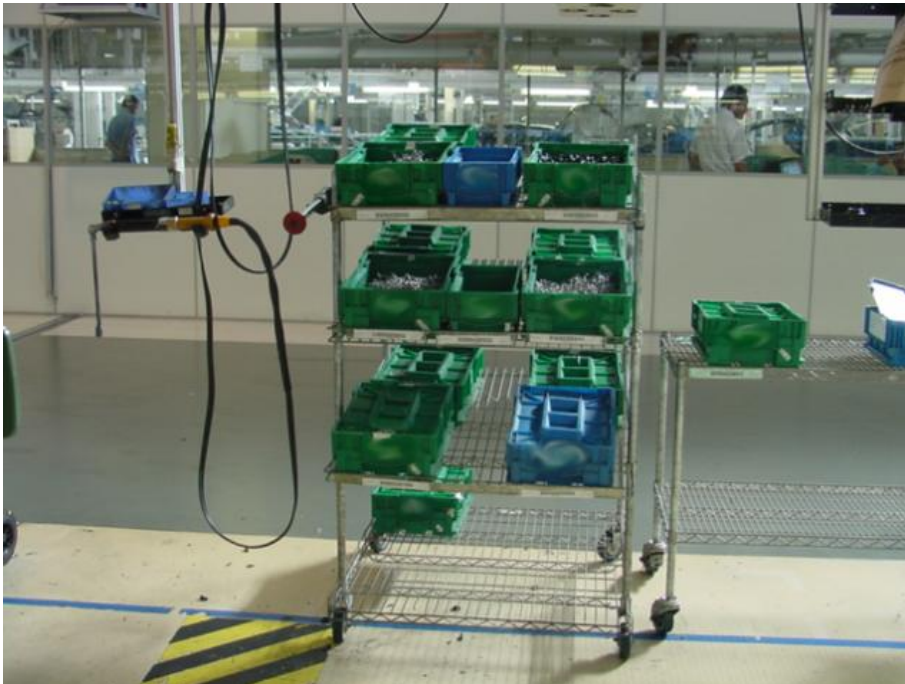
Abastecimento de peças ergonomicamente planejado
